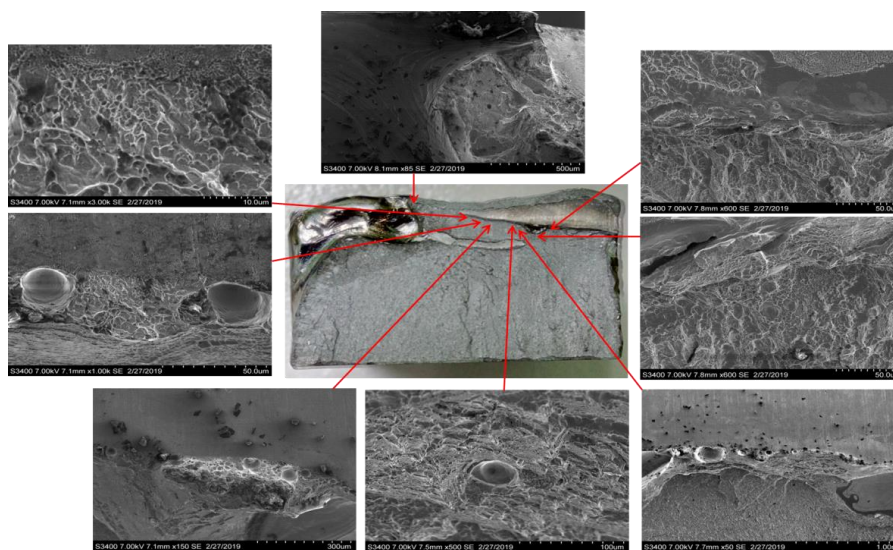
Фрактография изломов по фронту сварочной ванны (ВТ 20)
